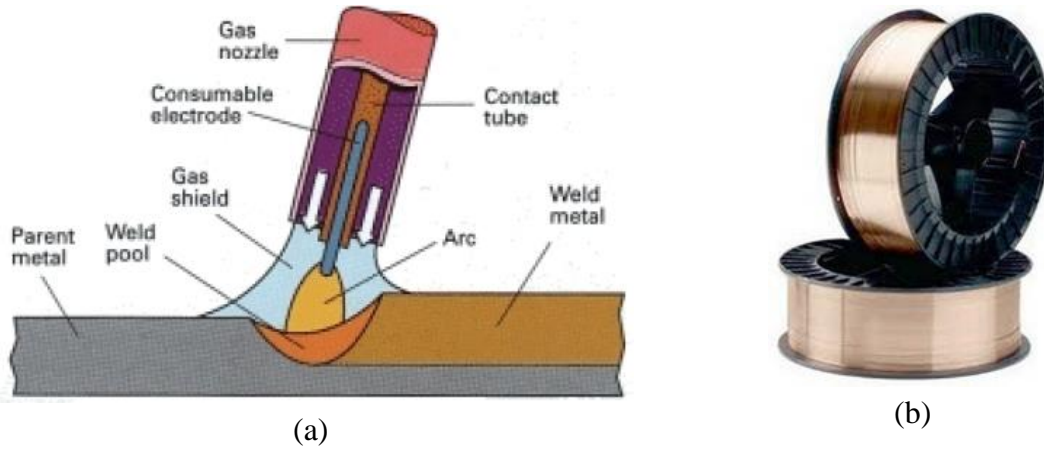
(a) Processo de soldagem a arco elétrico MIG/MAG [11]; (b) Eletrodo MIG/MAG.
